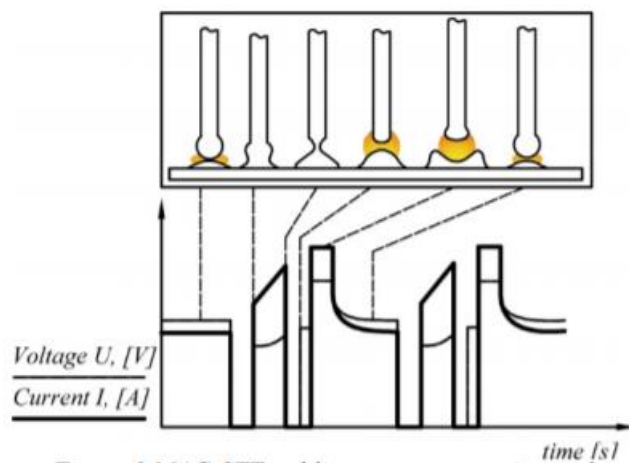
Процесс сварки STT – создание и перенос капли [8]
